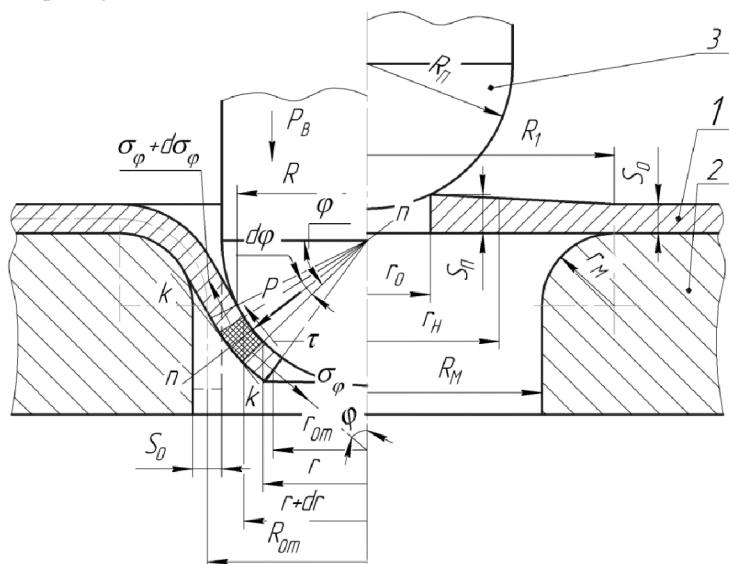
Розрахункова схема відбортування : 1 – заготовка, 2 – матриця, 3 – пуансон
